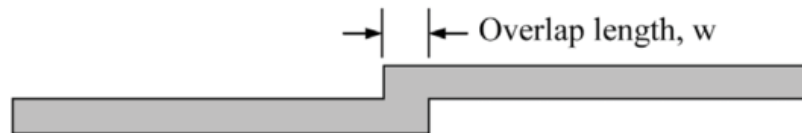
Paramètre d'intérêt sur un joint de recouvrement (overlap joint) [57]
